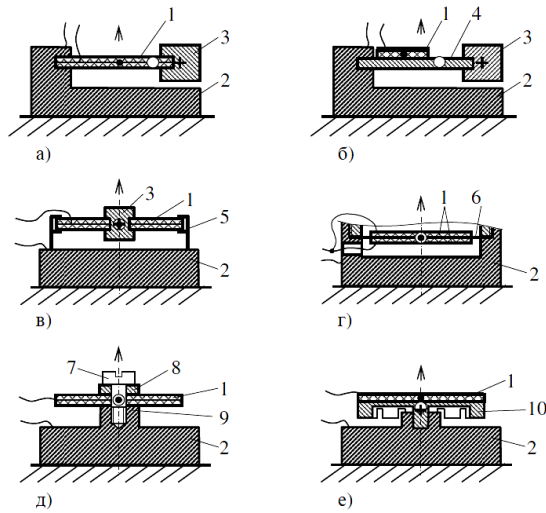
Схеми розміщення ЧЕ у конструкції ПГ АГС: 1 – ПЕ; 2 – основа; 3 – ІМ; 4 – балка; 5 – стійка; 6 – пластина; 7 – гвинт; 8, 9 – опора; 10 – пластина із інерційними елементами
